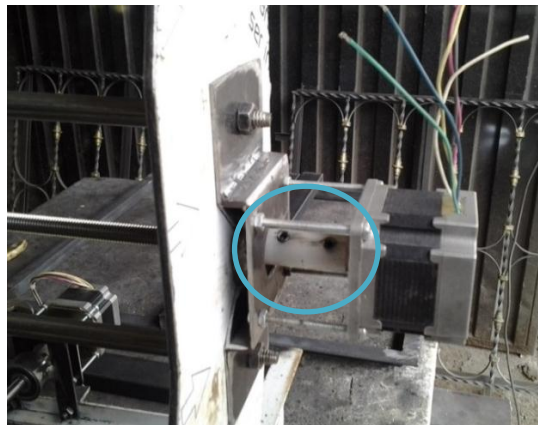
Sistema de acople del Tornillo sin fin y el Motor PAP
